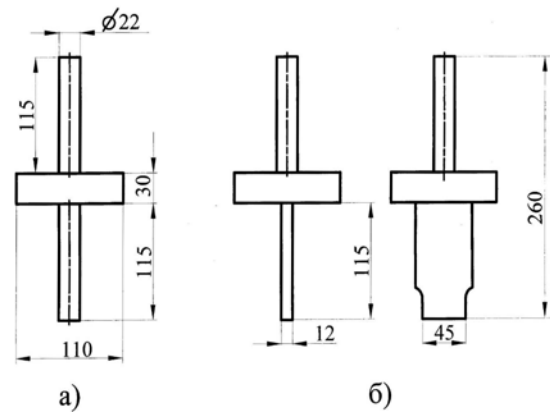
Кресленик модельного зразка зварного з'єднання з циліндричною (а) та призматичною (б) захватними частинами
